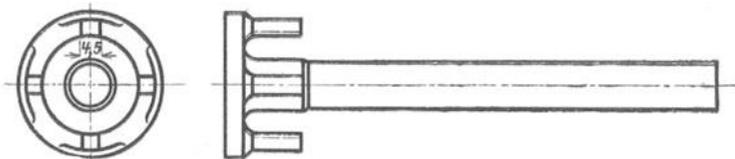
und 250. Kegel mit ausgefrästen Führungsrippen.
